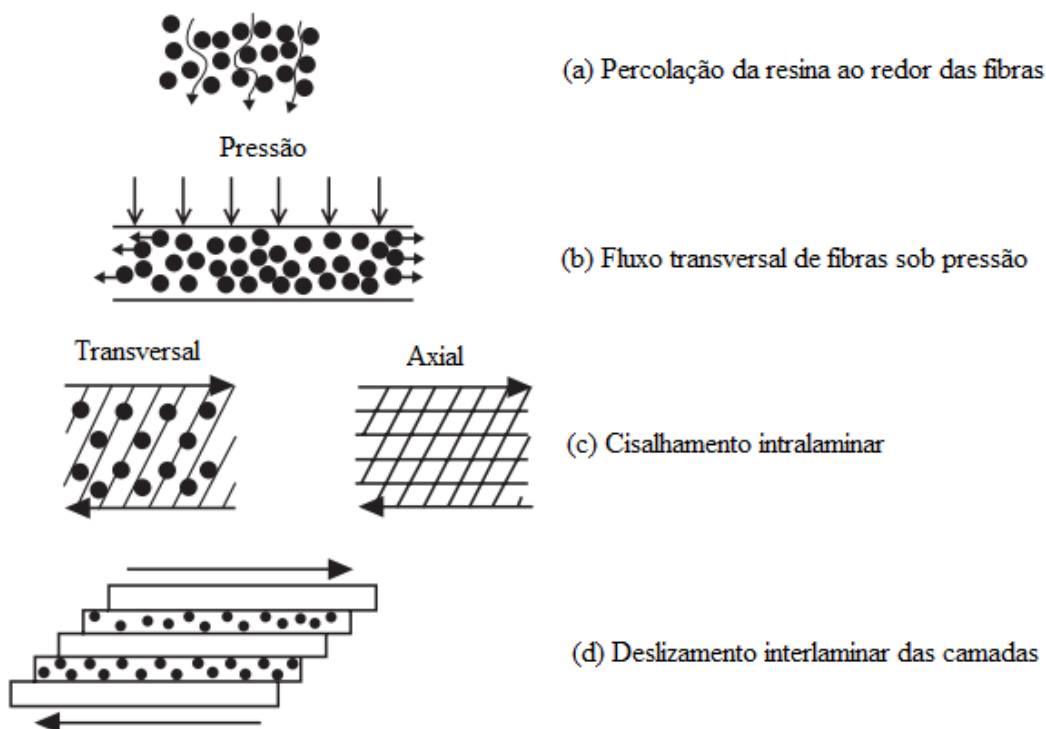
Etapas de processamento via moldagem por compressão a quente.
